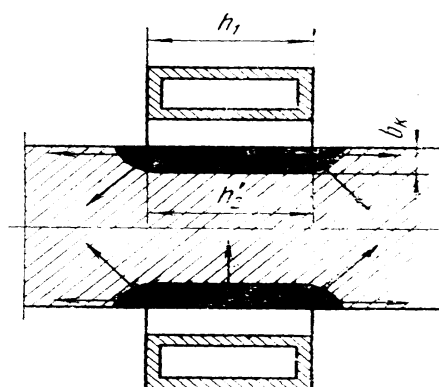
Система индуктор – деталь установки одновременного нагрева
